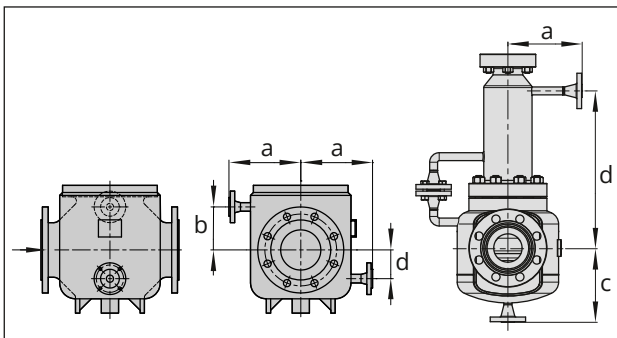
Typ 3251 med värmejacka · Dimensioner på begäran
